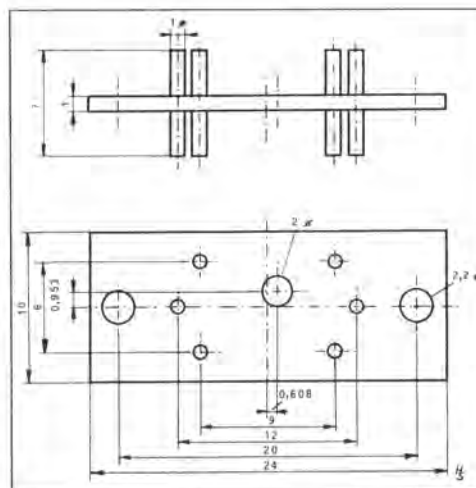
Bohrlehre für die Lagerbohrung im Querbolzen
